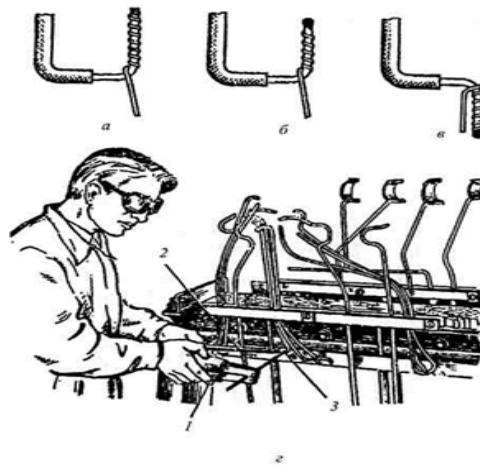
Операції зварювання відводів обмотки ВН: а - підготовка до зварювання; б — виконання зварювання; в - підготовка до ізолювання; г - приварювання відводу до кінця обмотки; 1 - кліщі; 2 - захват з гачком; 3 - відвід, який приварюється
